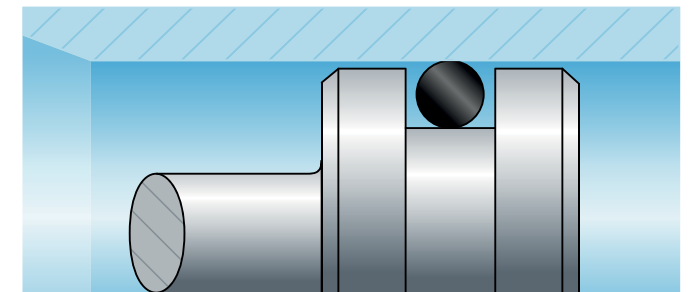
Nut im Innenteil („Kolbendichtung“): O-Ring radial verpresst
